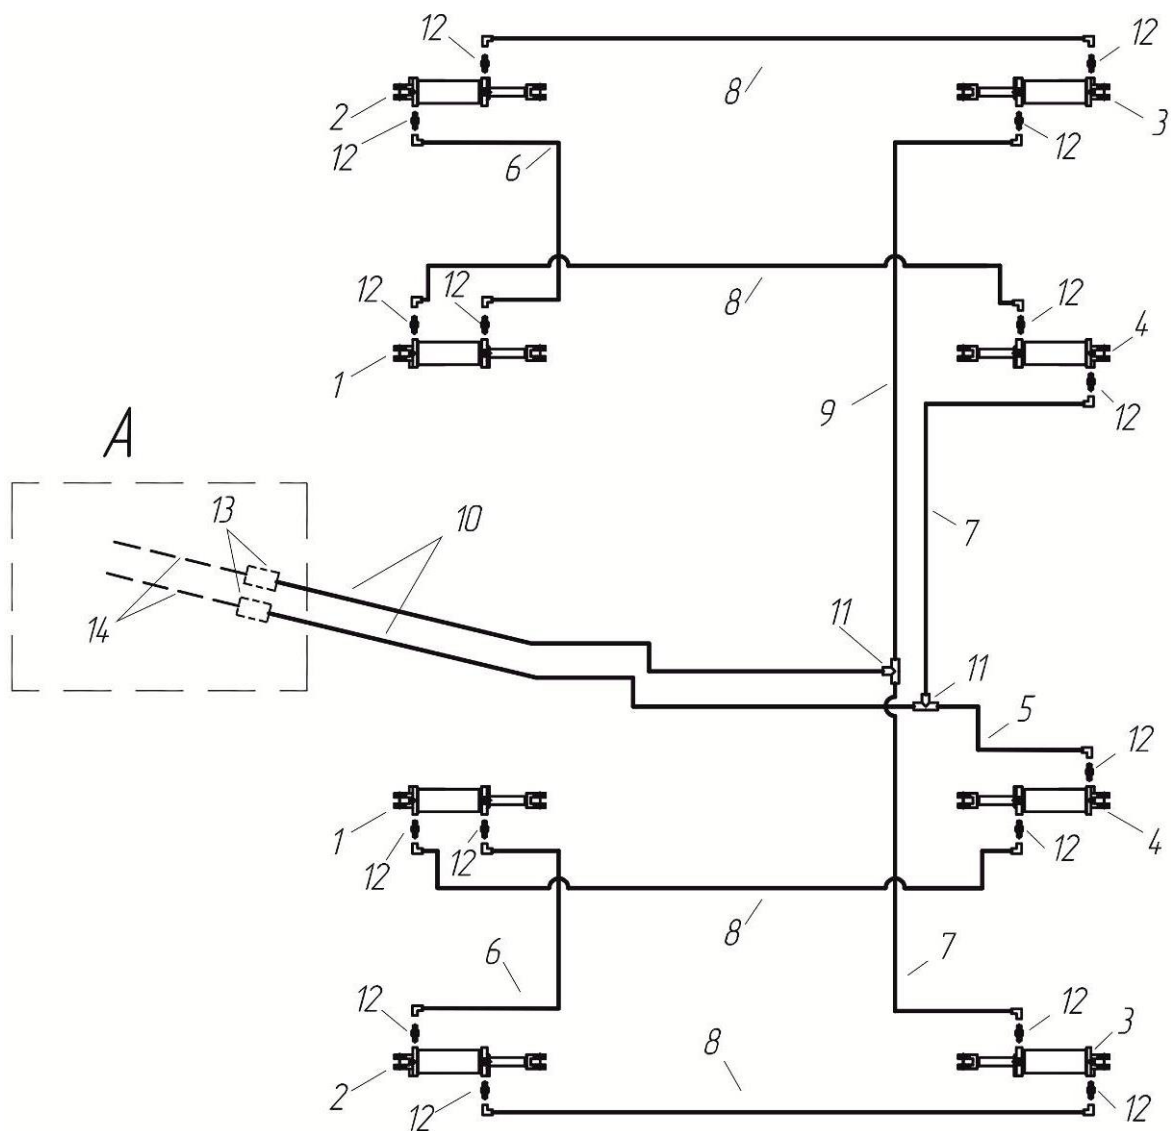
Схема установки гидроцилиндров и шлангов ПК-6.1 (гидросистема регулировки глубины заделки)
